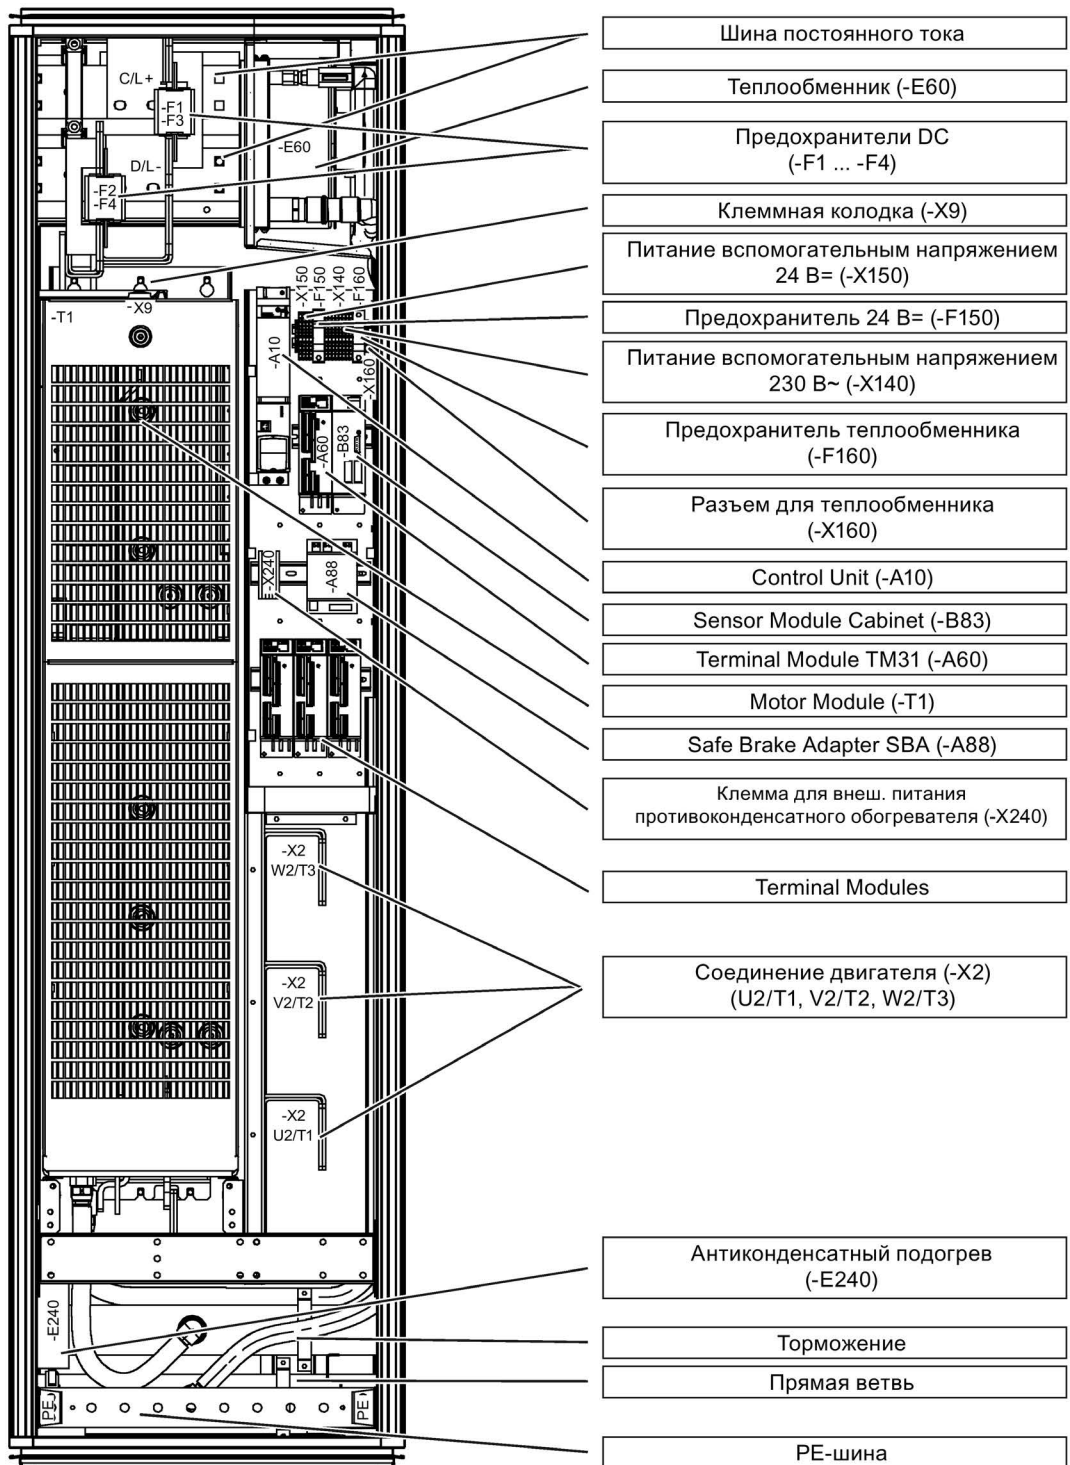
Конфигурация модуля двигателя (типоразмер JXL, без опций двигателя)
